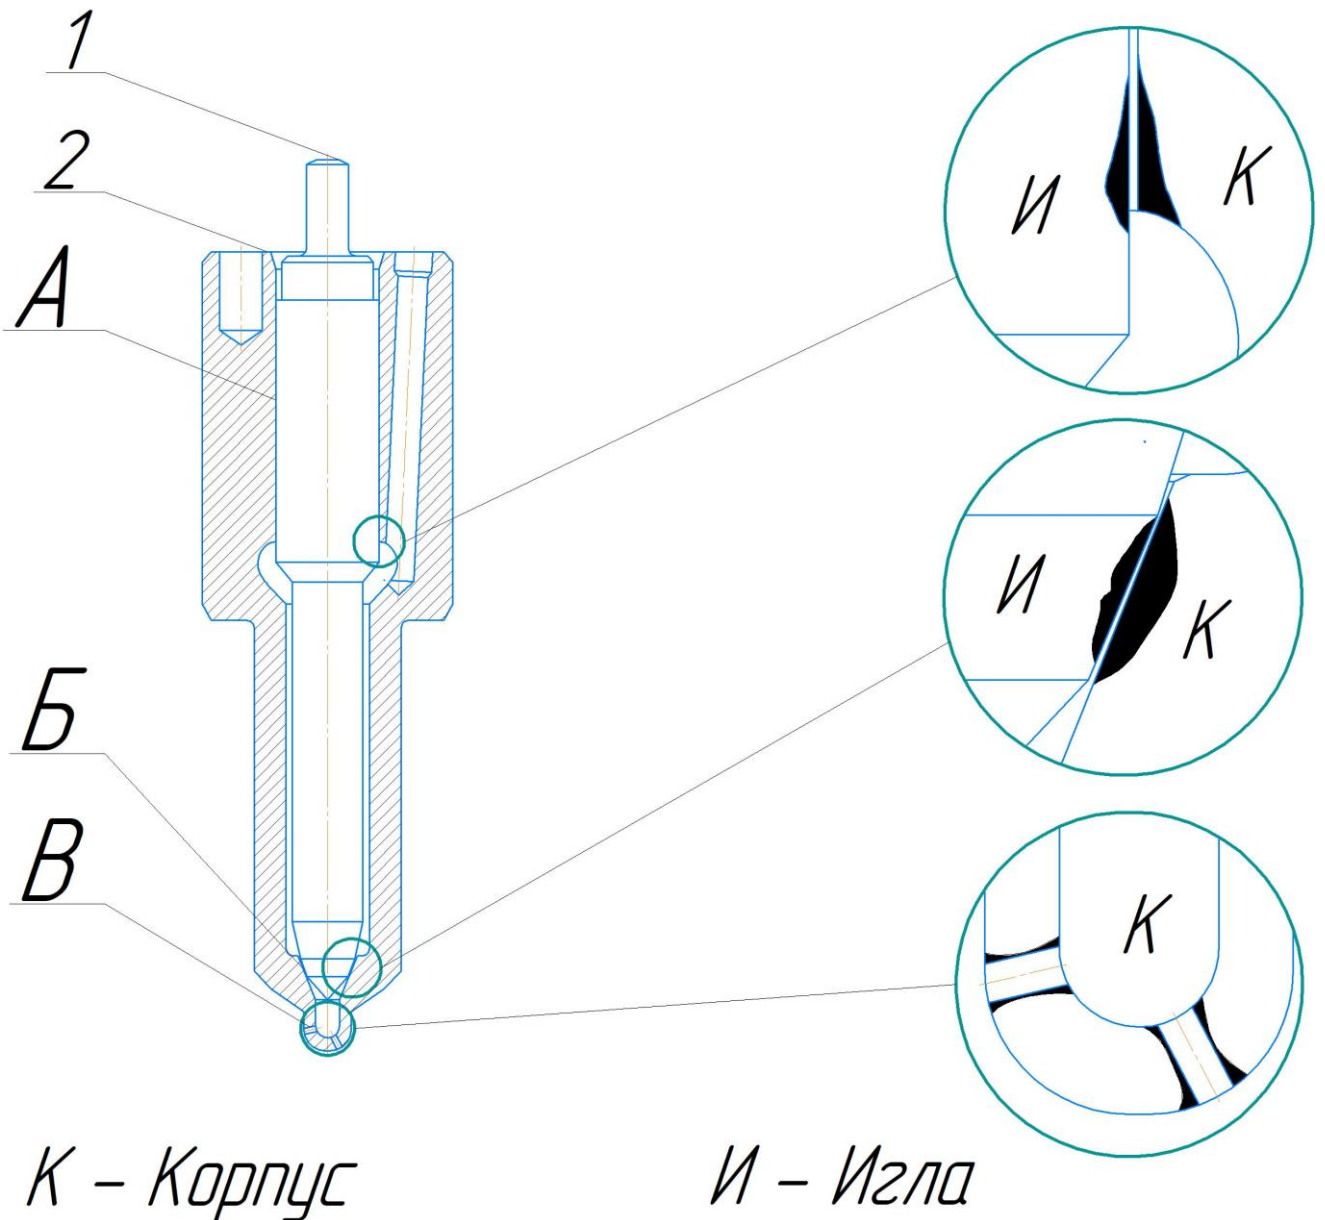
Дефекты (износ) иглы и корпуса распылителя [20]:
